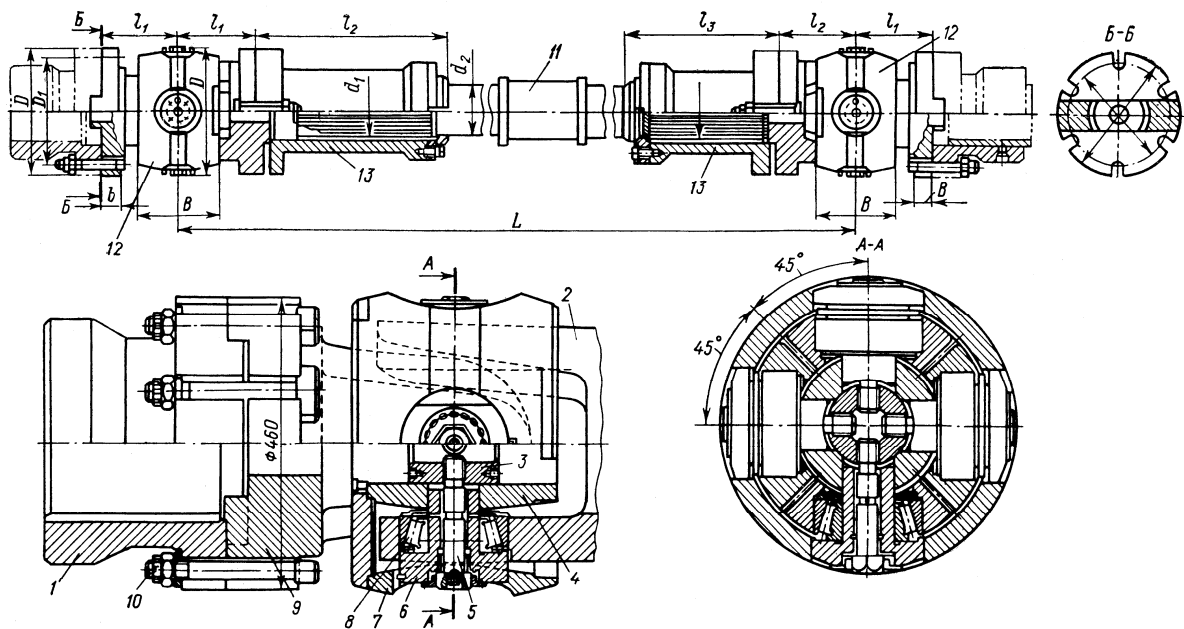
Універсальний шарнірний штиндель хрестовинного типу [5]:
